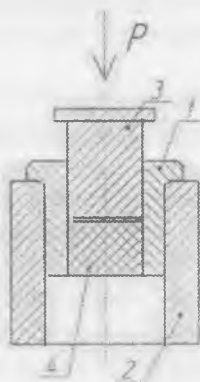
Схема проведения испытаний с приспособление в сборе (1 – матрица; 2 – обойма; 3 – шток (пуансон); 4 – опытный композит; P – сдвигающая нагрузка)
